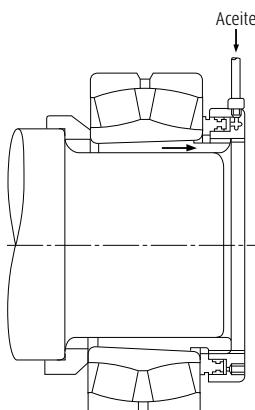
Desmontaje utilizando una Tuerca Hidráulica
